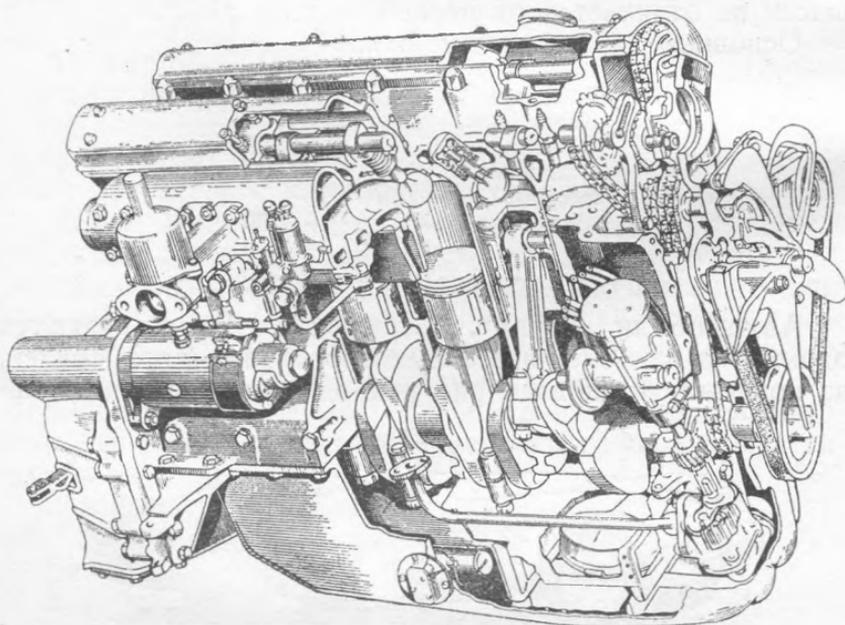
Двигатель автомобиля „Ягуар ХК-120 С“
